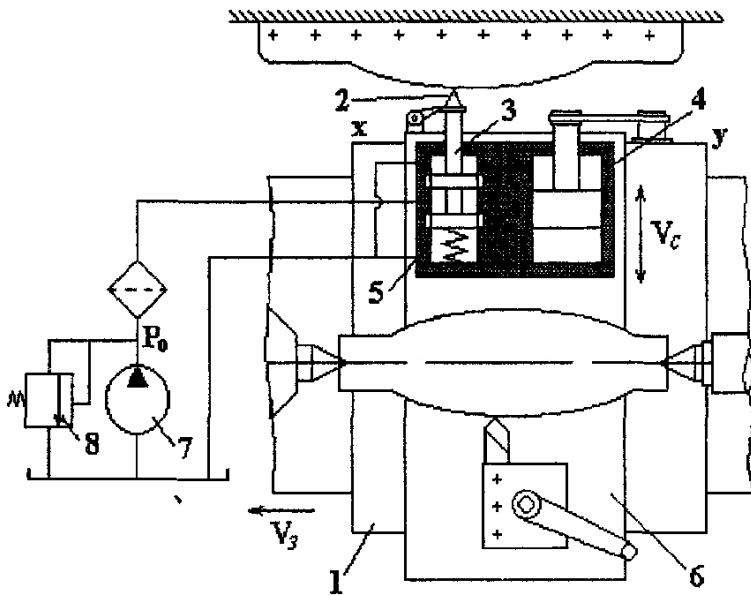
Схема сліdkуючої системи копіювально-токарного верстата
